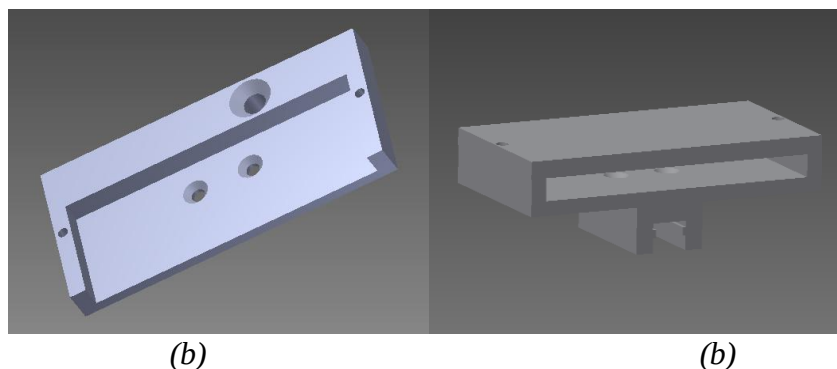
Hlavní deska přístroje s kolejnici ve 3D zobrazení: (a) deska, (b) detail
